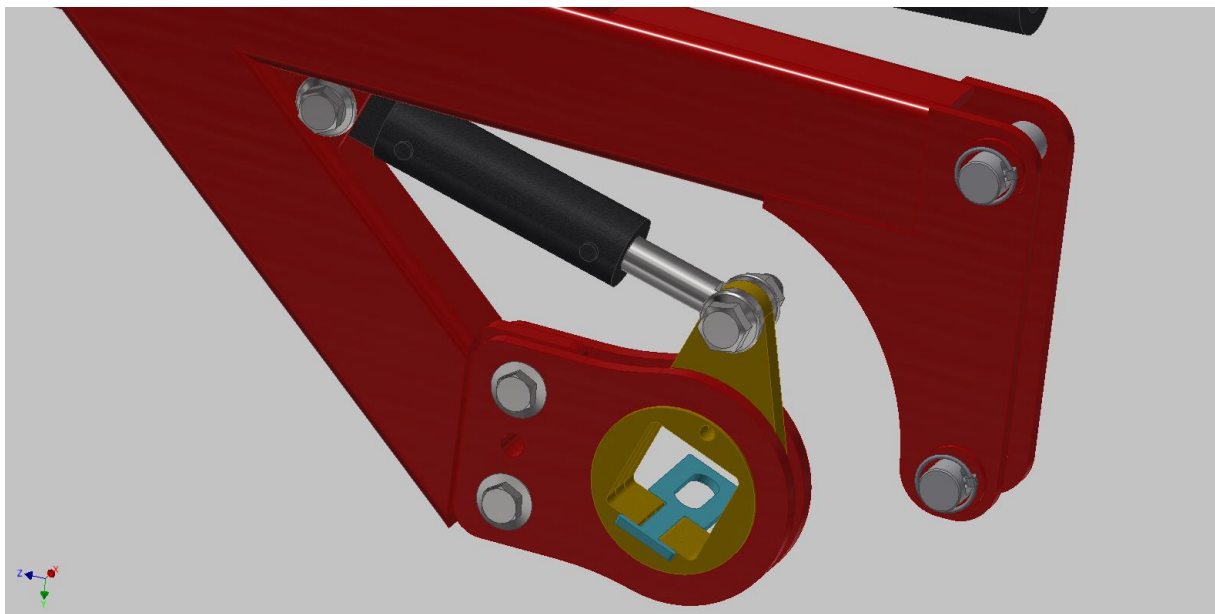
Brakett til feste av skiver som holder firkantrøret. Av forfatteren.
